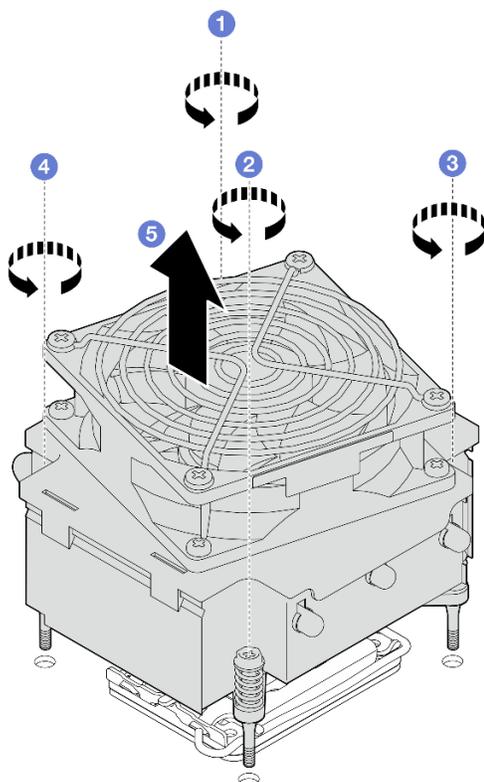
Retirer le dissipateur thermique et du module ventilateur
